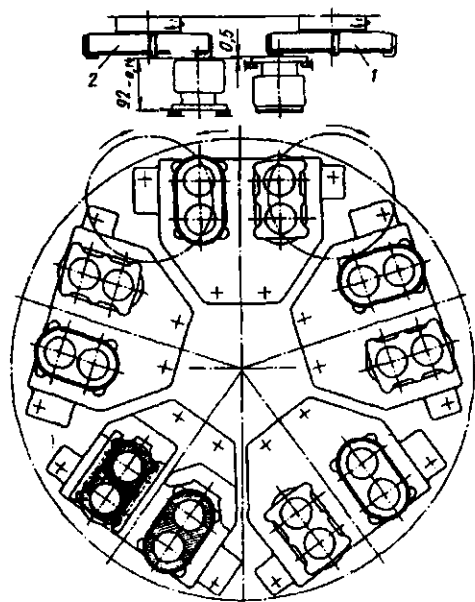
Схема фрезерования торцов заготовок на двухшпиндельном фрезерном станке с вращающимся столом: 1 – черновая фреза; 2 – чистовая фреза
